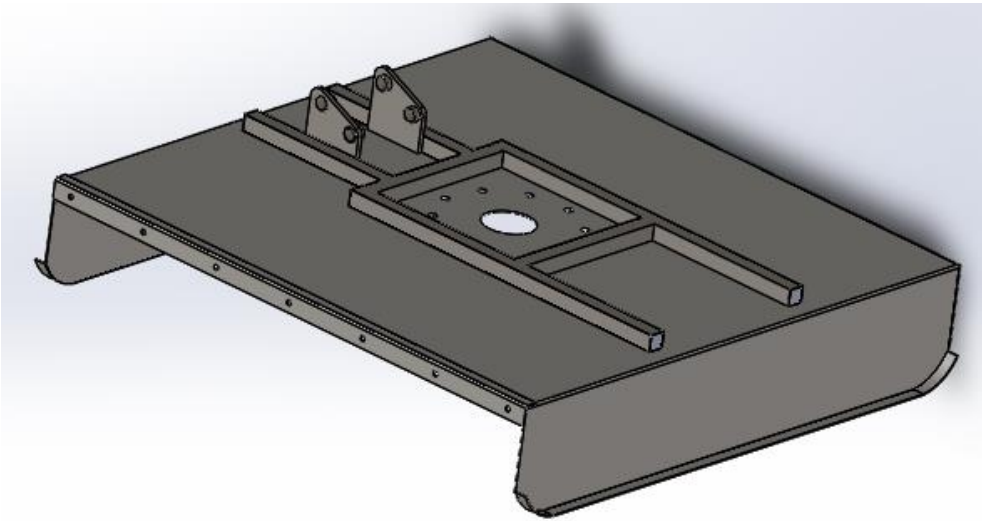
Vista isométrica del chasis soporte del rotor de corte.
